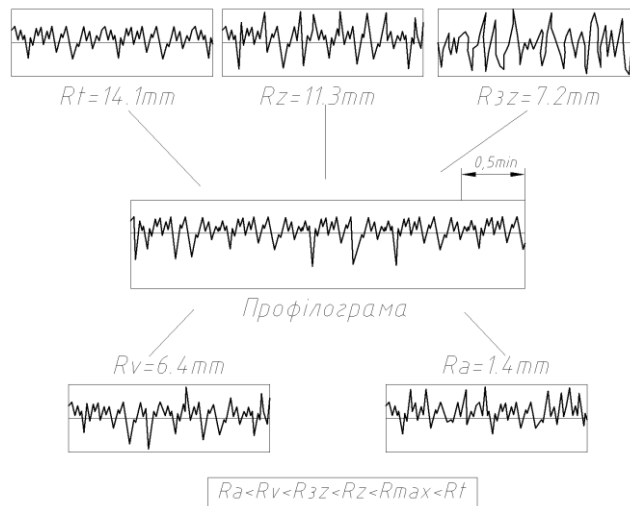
Геометричні параметри шорсткості робочого профілю поверхні гільзи циліндра після механічної обробки:
